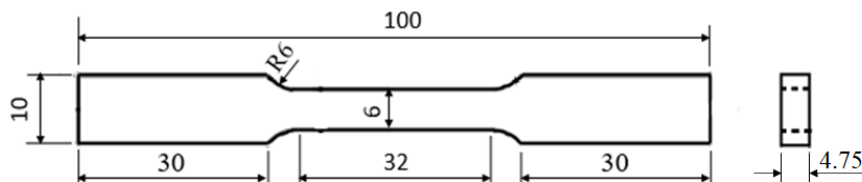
Corpo de prova para ensaio de tração (dimensões em mm).
